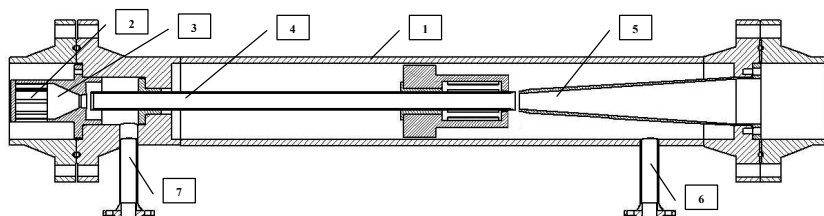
Термогазодинамический сепаратор: 1 — корпус; 2 — завихритель; 3 — сопло Лаваля; 4 — камера смешения; 5 — диффузор; 6 — патрубок отвода жидкости; 7 — патрубок подвода пассивного газ
